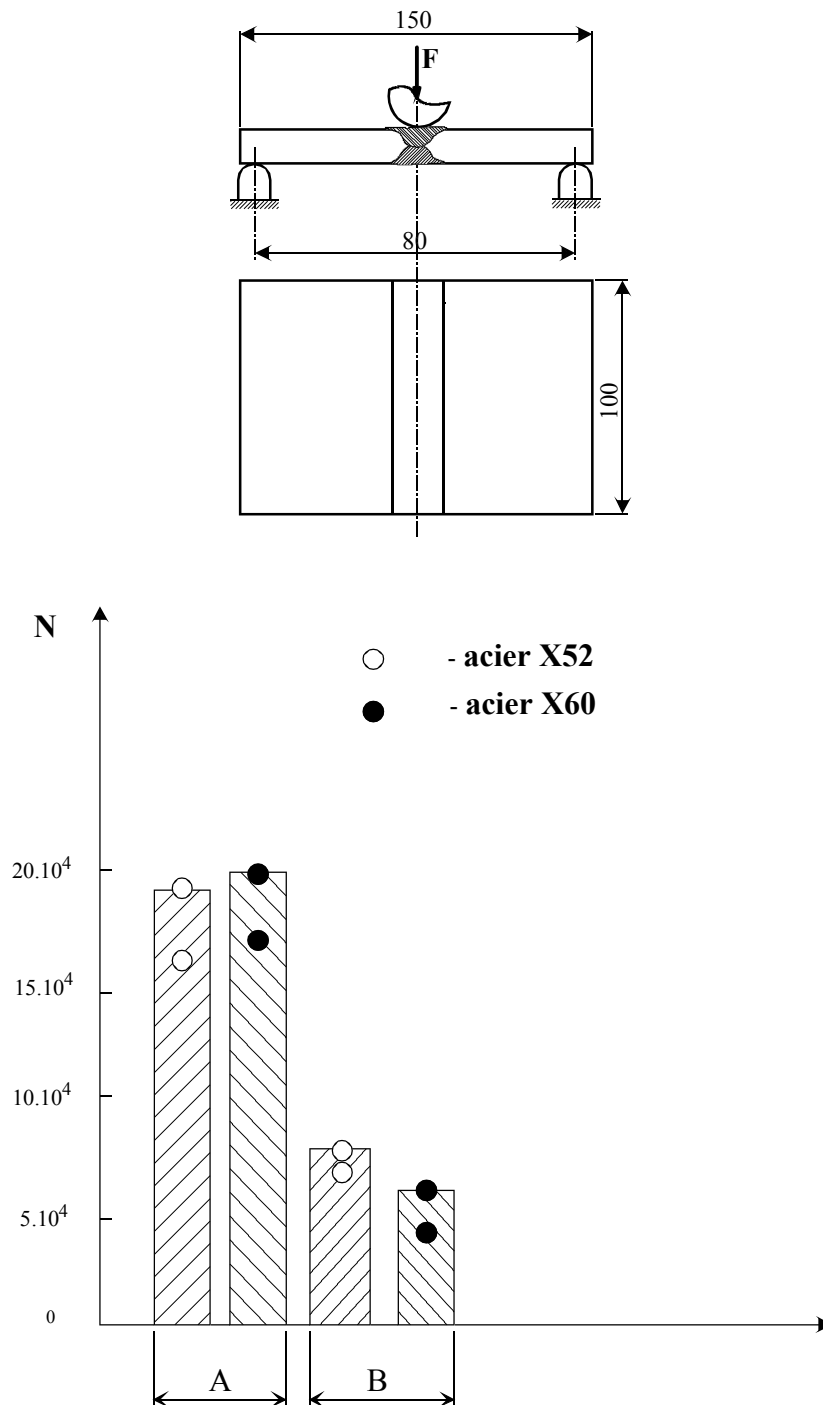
Durée de vie d'éprouvettes prélevées des joints de soudure des tubes en fonction de la forme du cordon et du régime des charges
